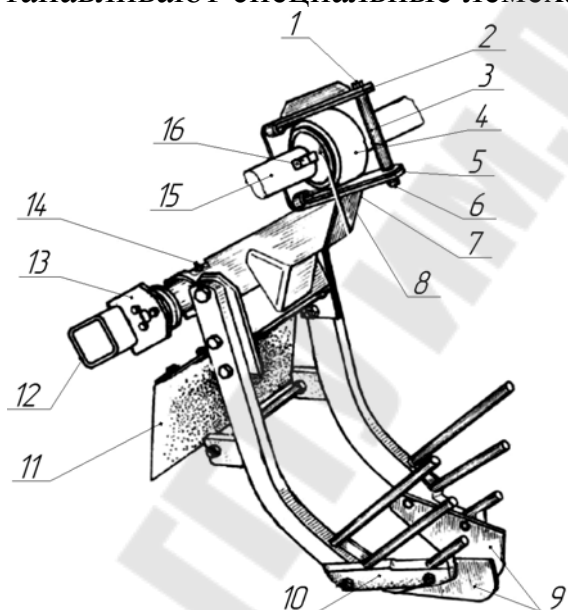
Копач: 1, 6 – детали крепления; 2, 5 – пластины; 3 – втулка; 4 – корпус эксцентрика; 7 – опора; 8 – эксцентрик; 9 – лемеха; 10 – стойка с прутками; 11 – ограждение; 12 – балка рамы; 13 – кронштейн; 14 – масленка; 15 – вал эксцентрика; 16 – шпонка
